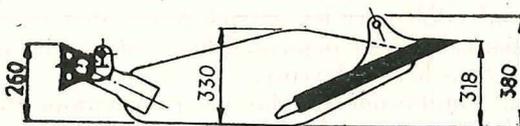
Racloir « Thomson » a) plan et coupe;
